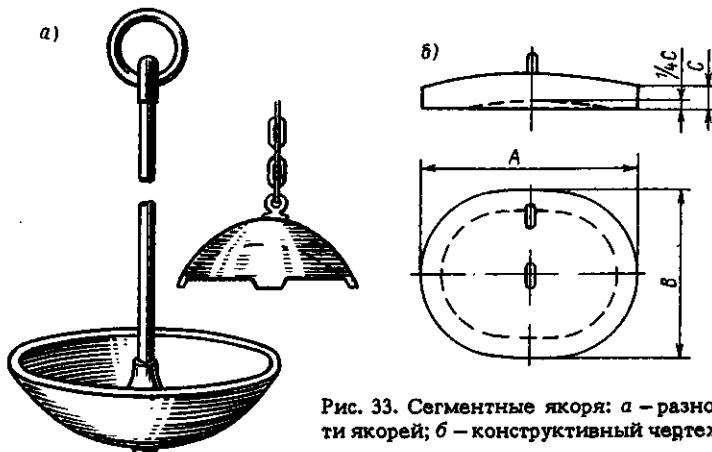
Сегментные якоря: а — разновидности якорей; б — конструктивный чертеж
